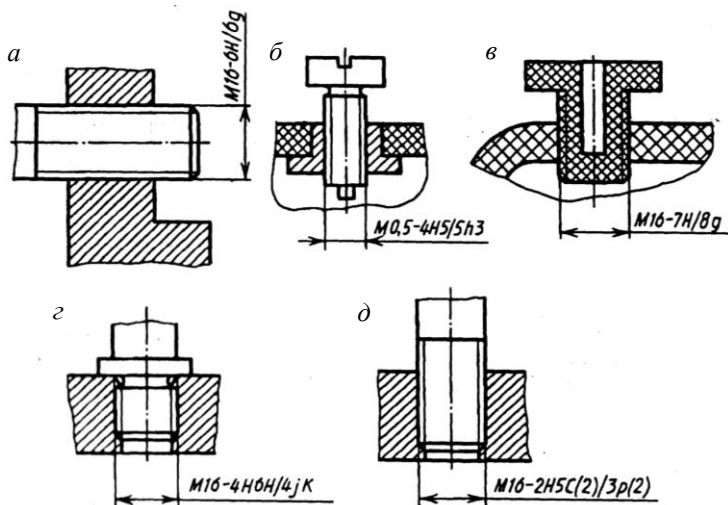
Условные обозначения посадок в резьбовых соединениях с метрической цилиндрической резьбой:
